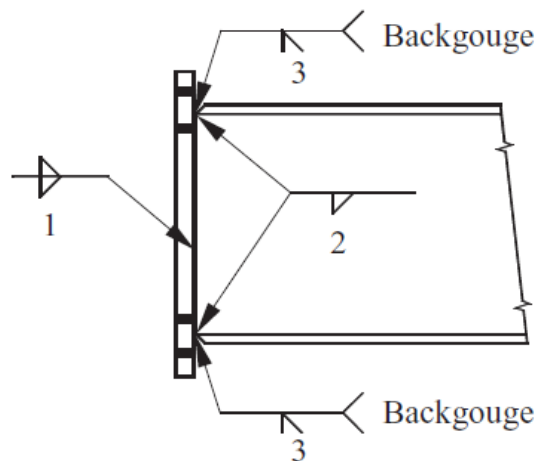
Recomendaciones para el proceso de soldadura.
